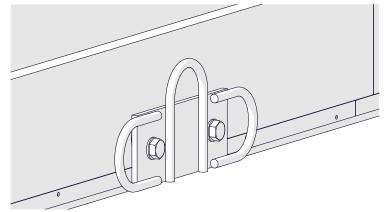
Внешний вид пластины транспортирования ЖД
